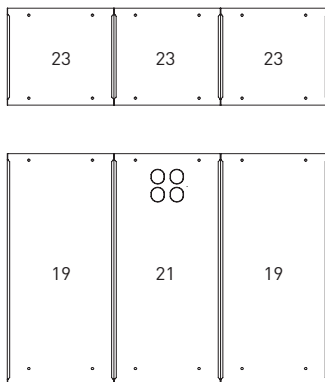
Schräge, aufgelegt – Ansicht von oben
